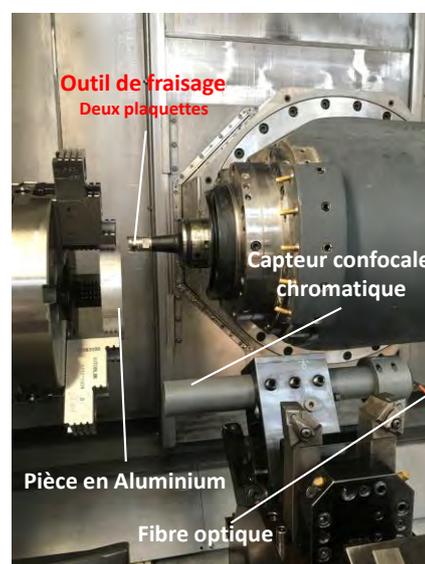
Intégration du capteur confocale chromatique à la machine CNC
